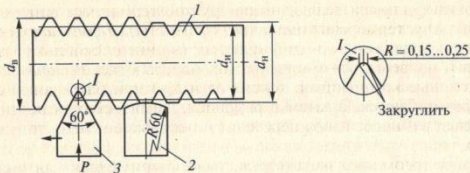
Схема восстановления деталей электромеханическим способом: 1 — деталь; 2 — сглаживающий инструмент; 3 — высаживающий инструмент; d_n — диаметр изношенной детали; d_n — диаметр детали после высадки; d_n — номинальный диаметр детали; P — усилие прижатия инструмента
